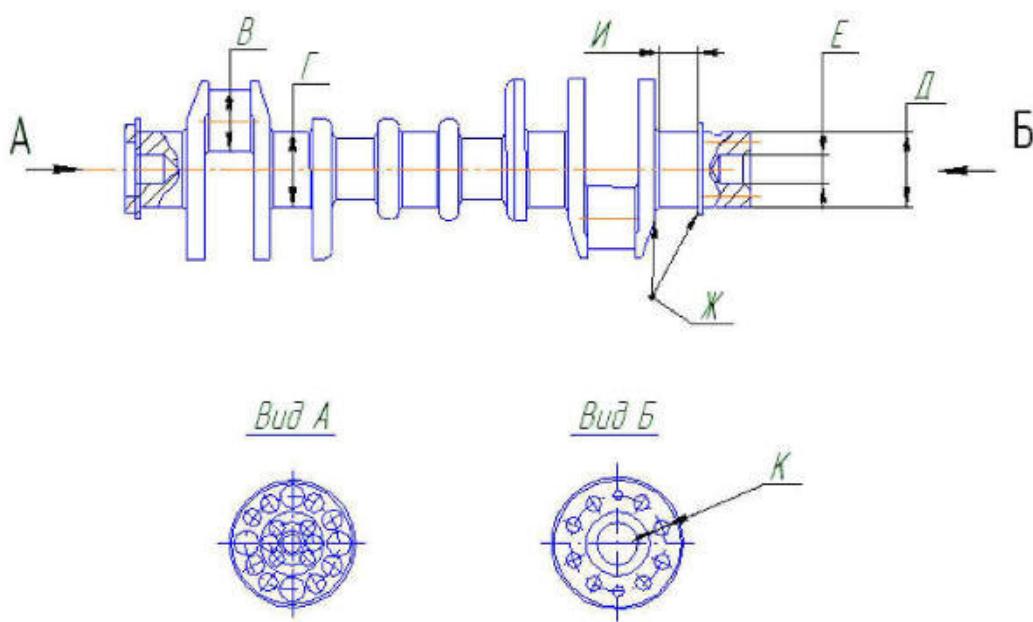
Дефекты коленчатого вала автомобиля КамАЗ-740.
